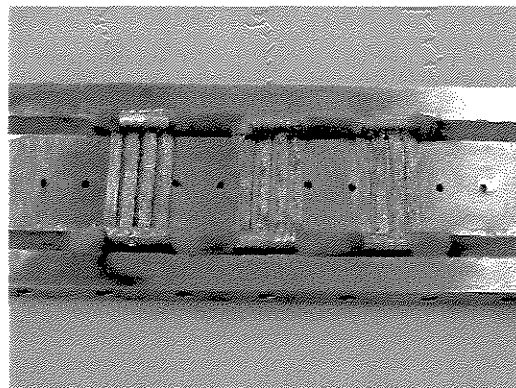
Tiras metálicas fixadas ao dispositivo.
